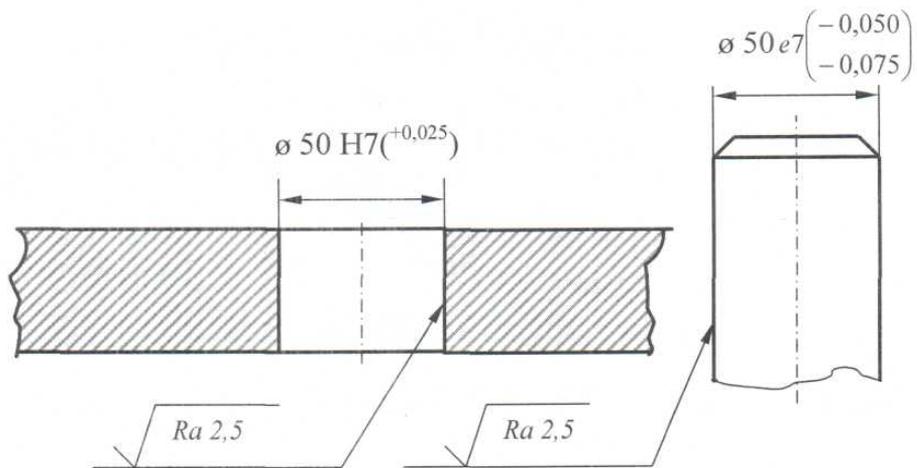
Обозначение допусков размеров на деталировочных чертежах
